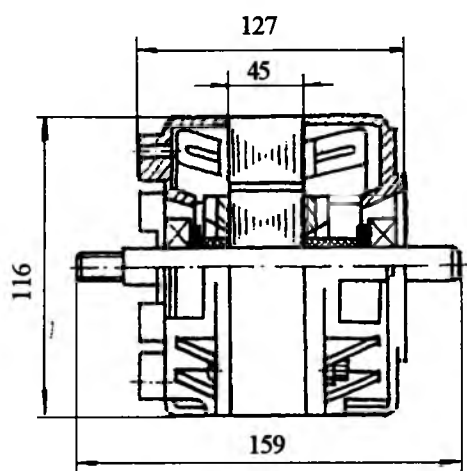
Двигатель КД 120-4/56 РМ6 классической конструкции
